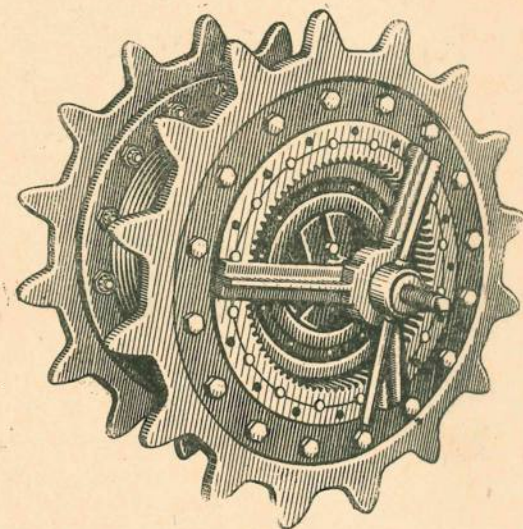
Выпрессовка шарикоподшипника из корпуса ведущего колеса
